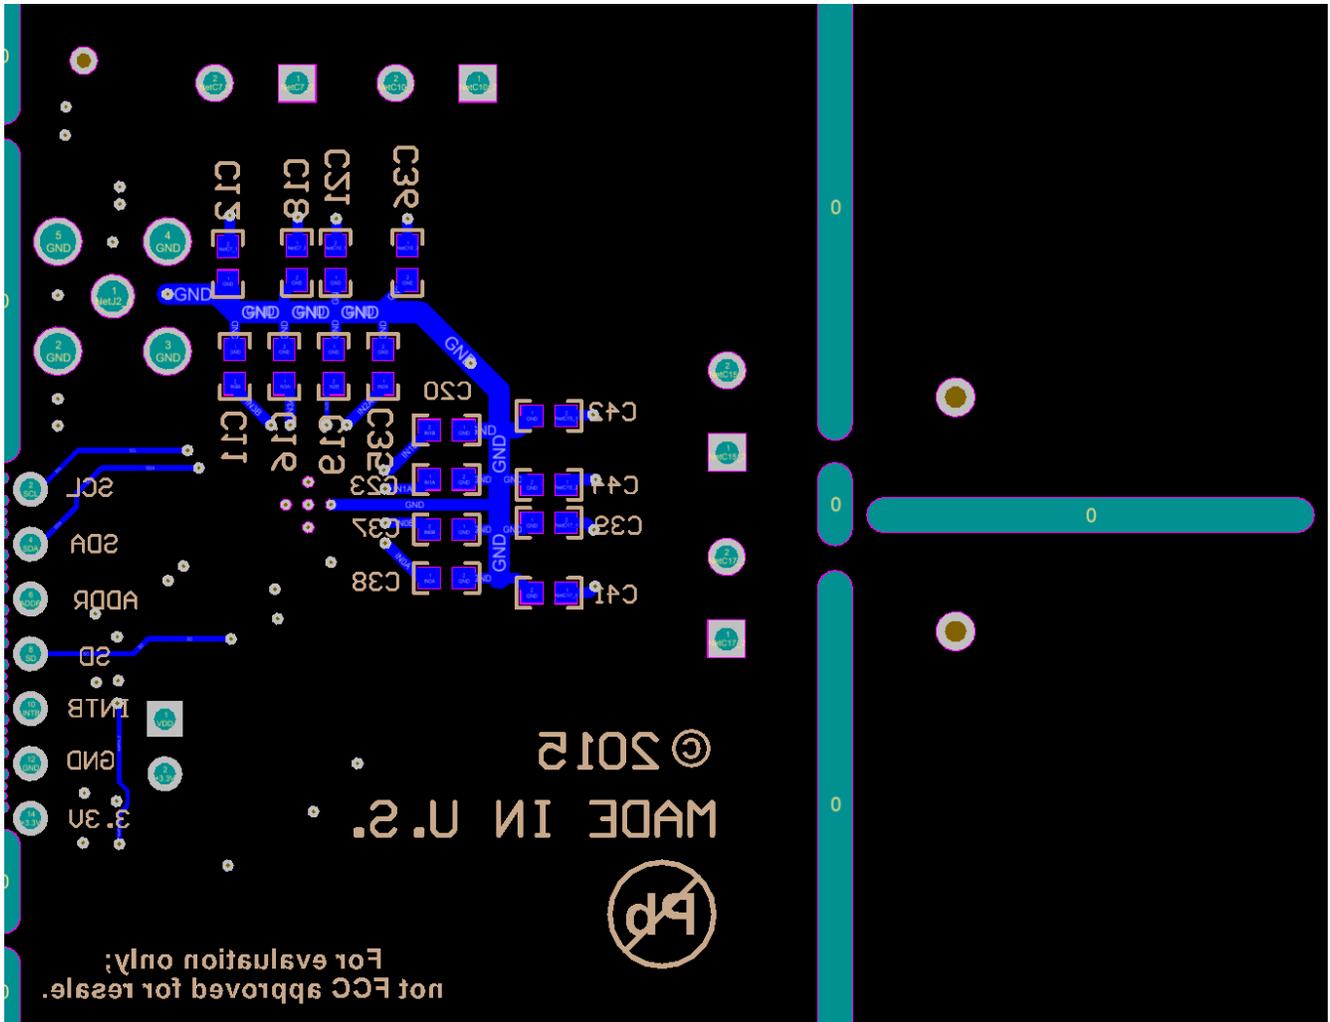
Example PCB Layout: Bottom Layer (Signal)
